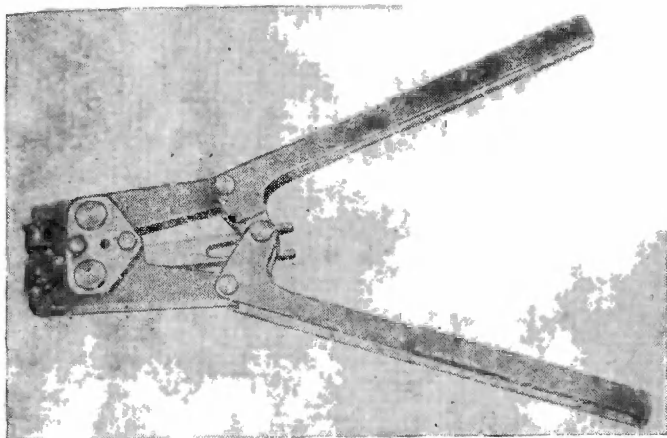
Ручные клещи (пережим) для холодной сварки металлических штенгелей.
